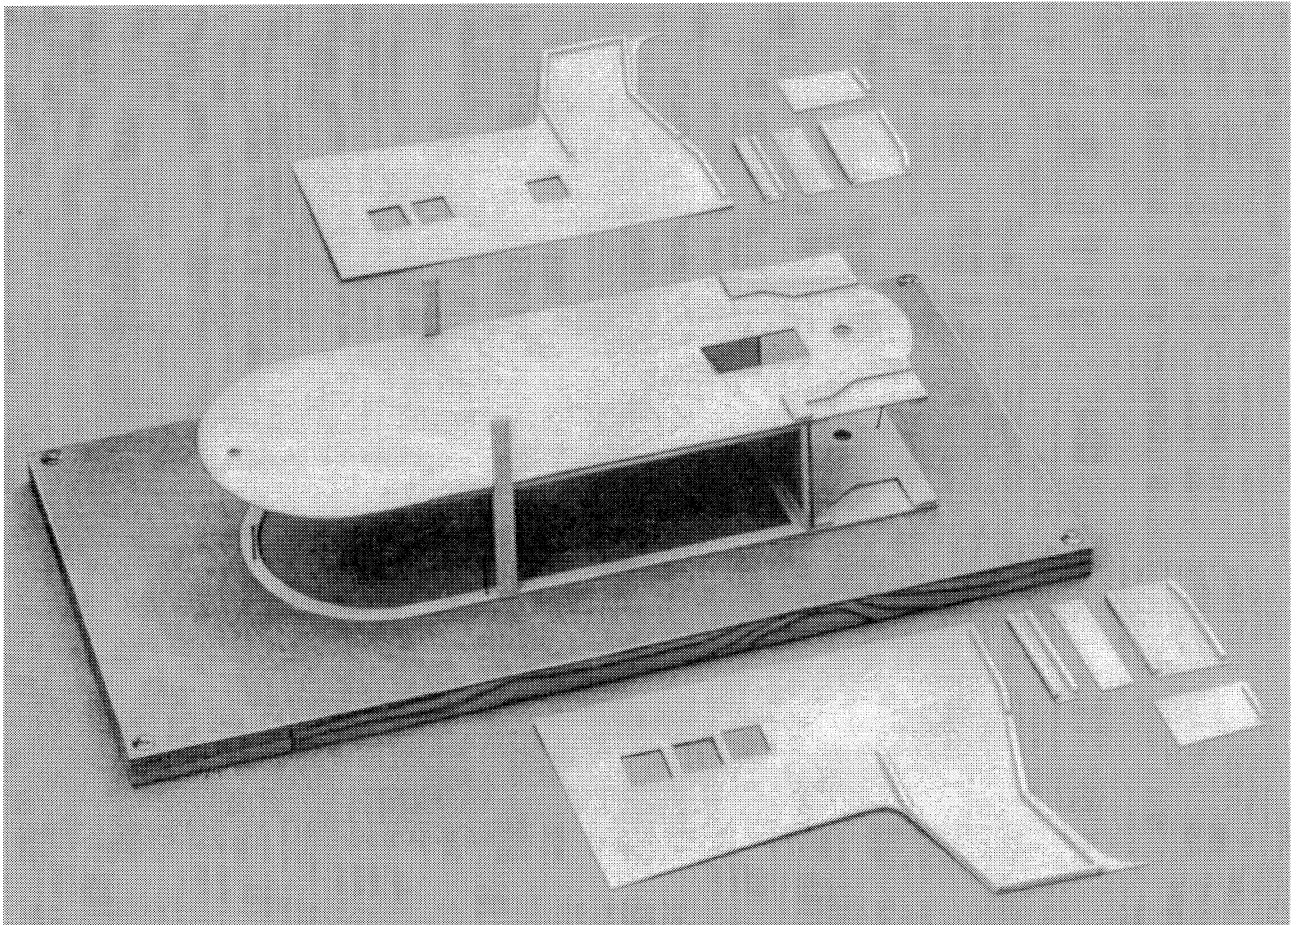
Der Aufbau des Deckshauses wird auf einem Baubrett vorgenommen. Einige Teile liegen zum Ankleben davor.
